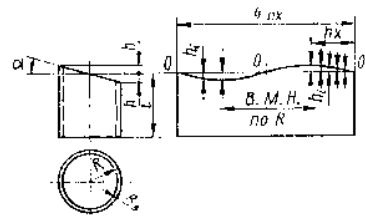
Построение развертки усеченной цилиндрической поверхности:
